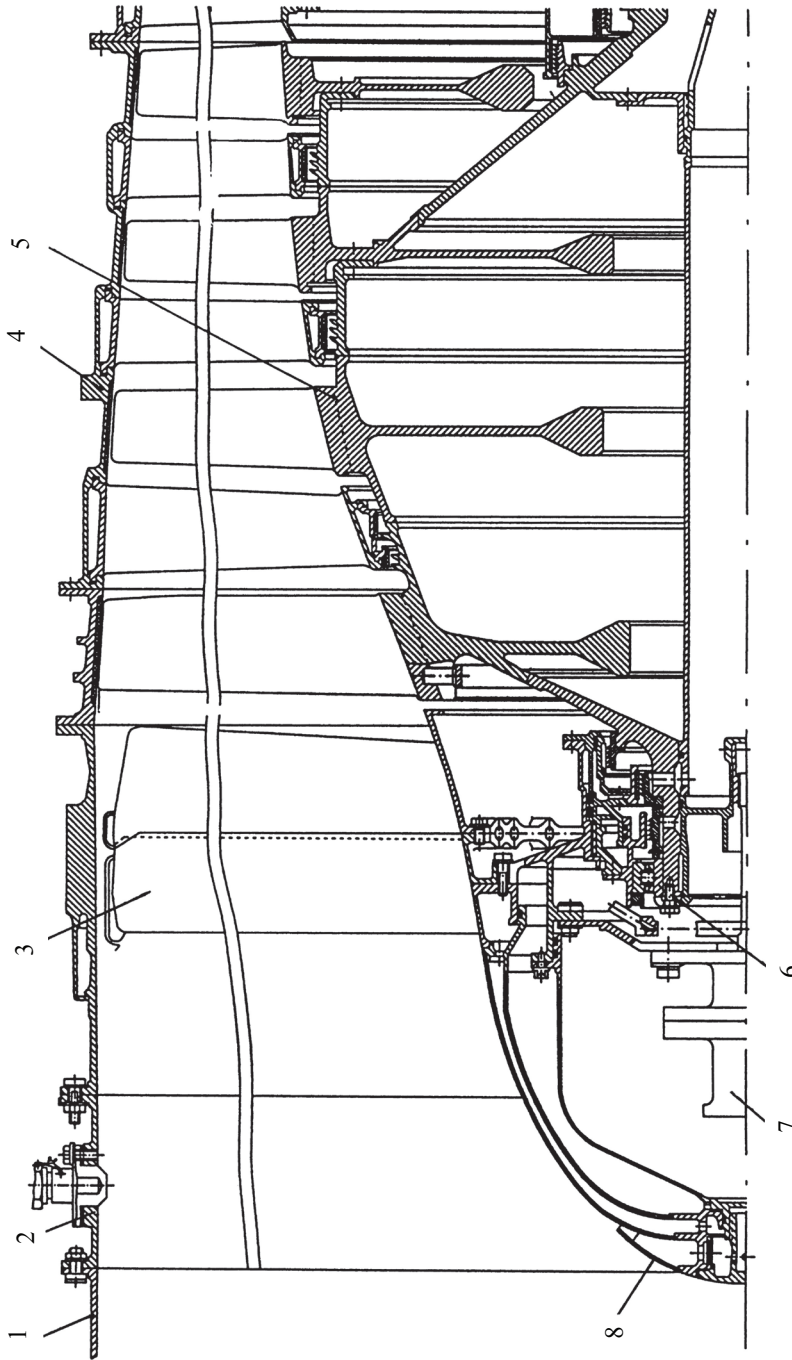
Компрессор низкого давления ГТД АЛ-31СТ:
